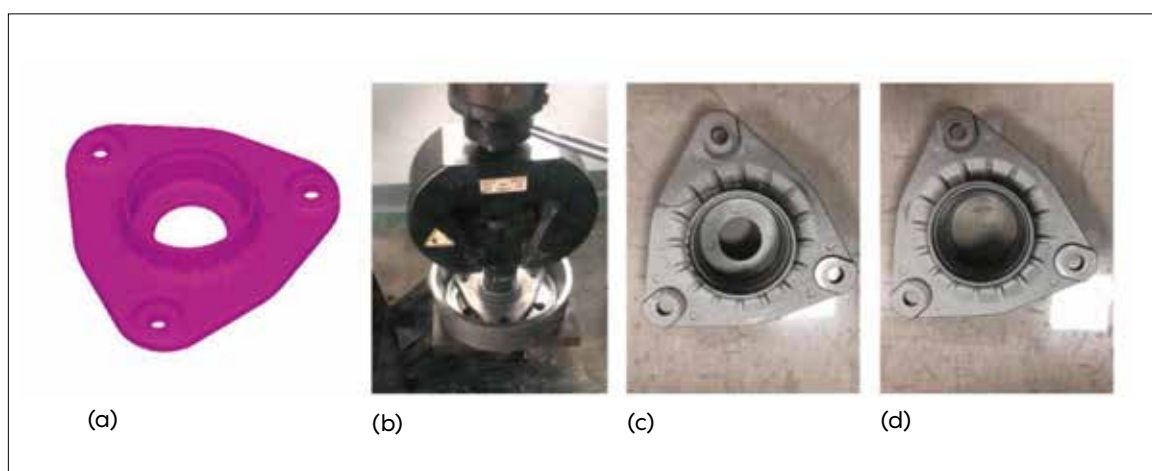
Modello CAD 3D (a) telaio di montaggio superiore (b) processo di test delle prestazioni (c) e (d) frattura della parte in alluminio dopo il test delle prestazioni.
